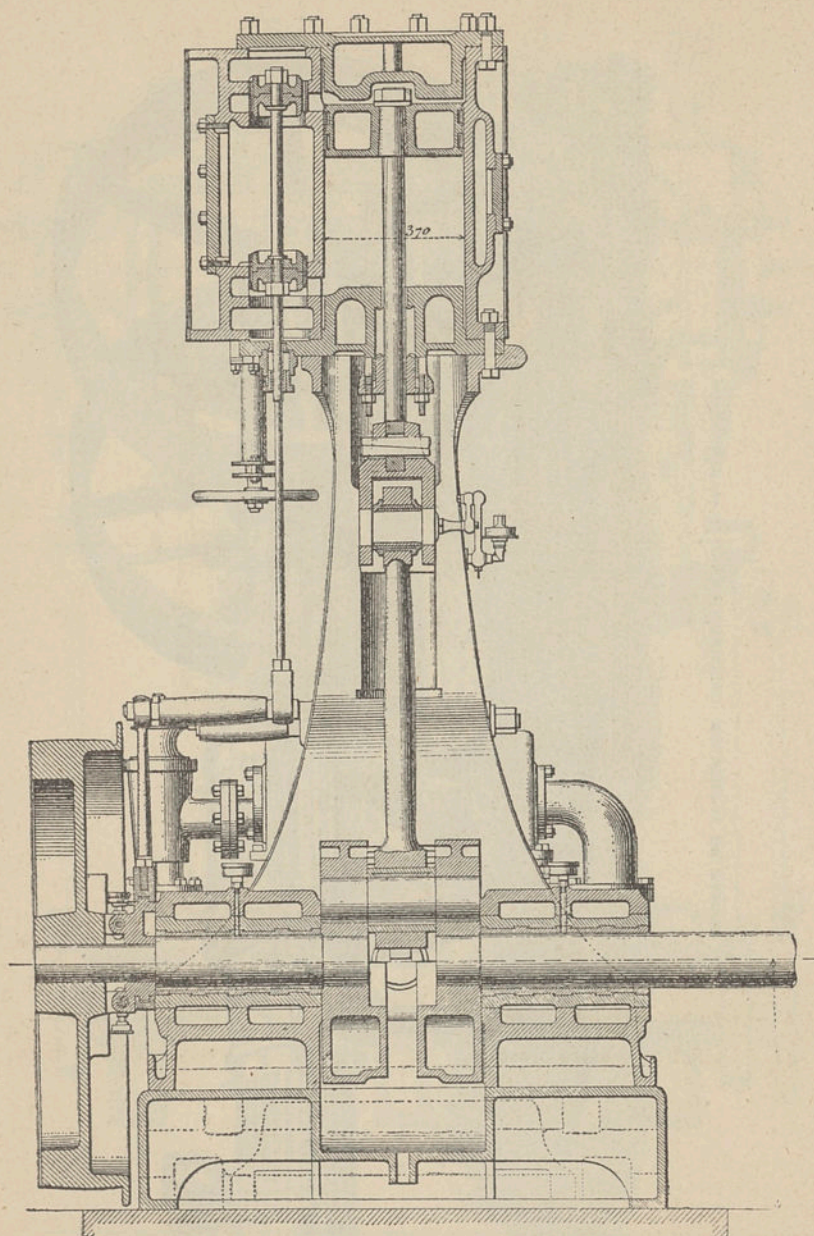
MACHINA DE PILÃO COM DISTRIBUIDOR CYLINDRICO
